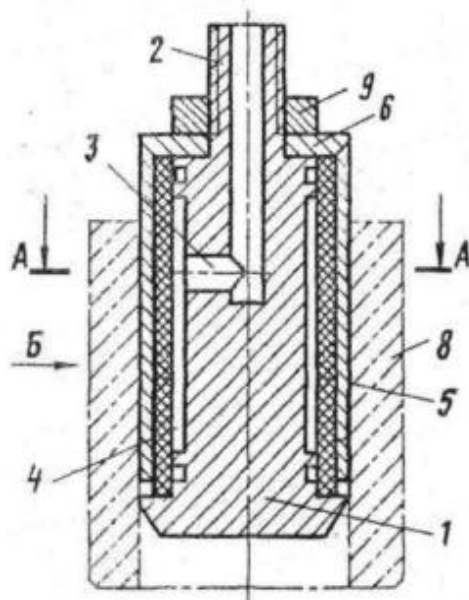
Камерний захоплювальний пристрій для транспортування циліндричних виробів, у яких є внутрішня порожнина
